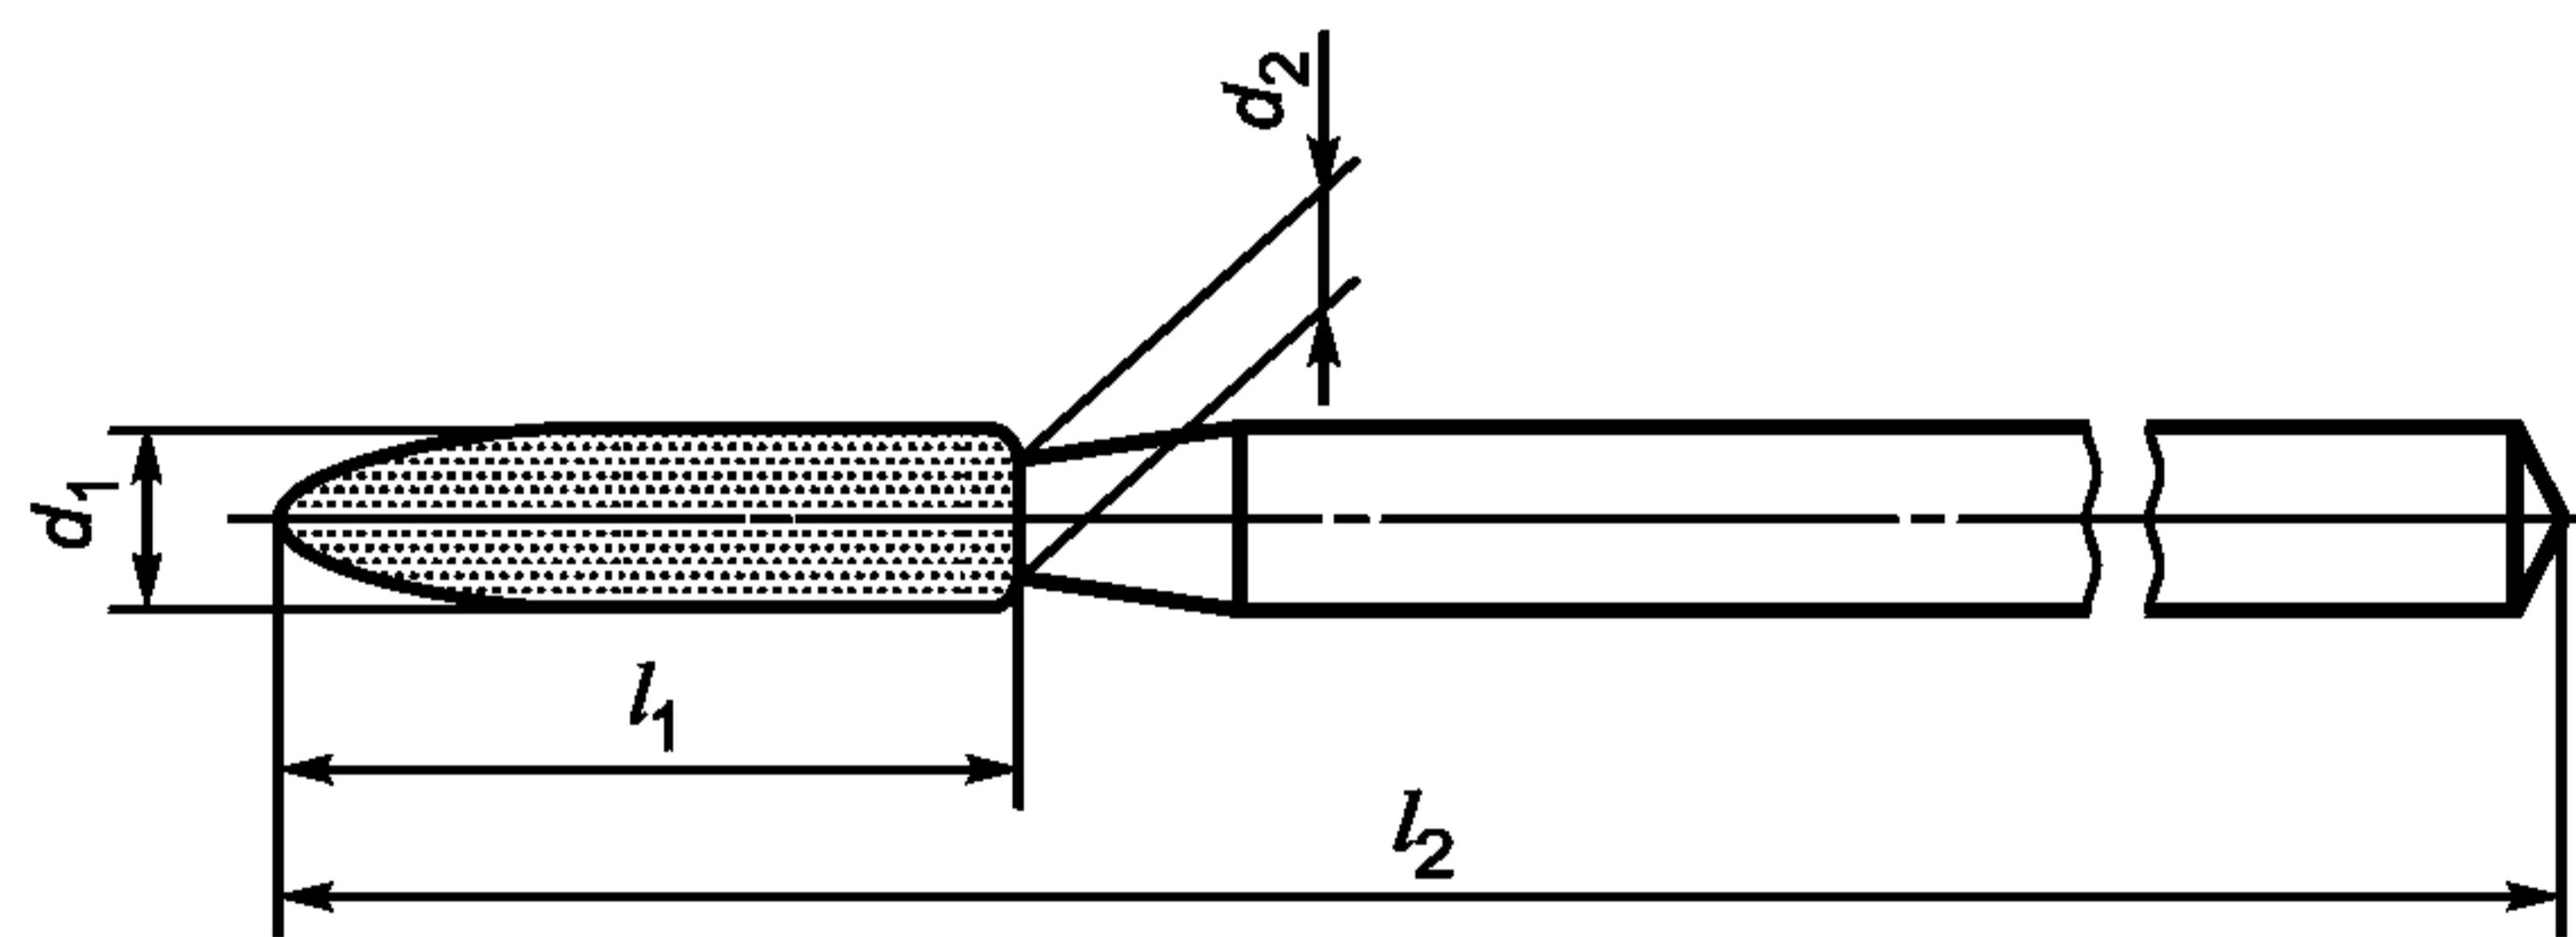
Цилиндрическая с огивальным концом рабочая часть с длиной головки 8,0 мм
